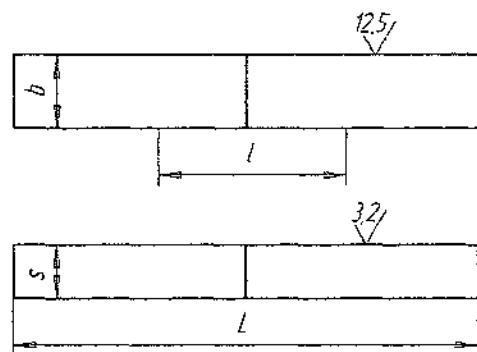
Образец для испытания сварного соединения на статический изгиб
